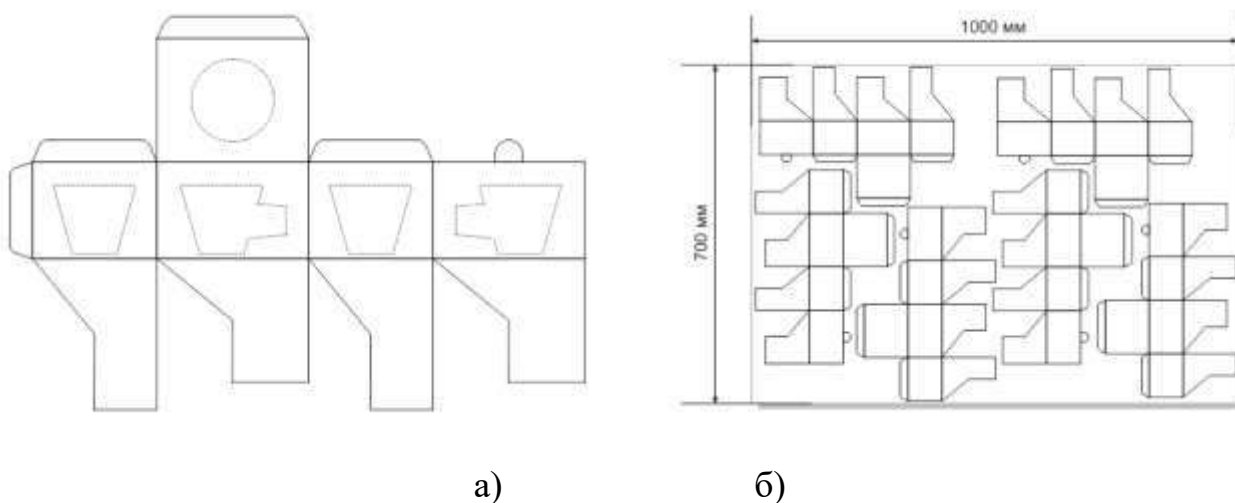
Підготовка до висікання заготовки коробки:
